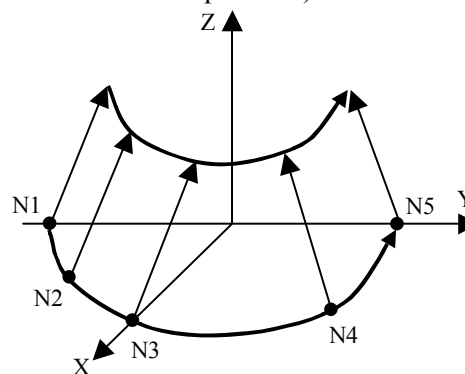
(c) Плавное управление (G43.4P3)
